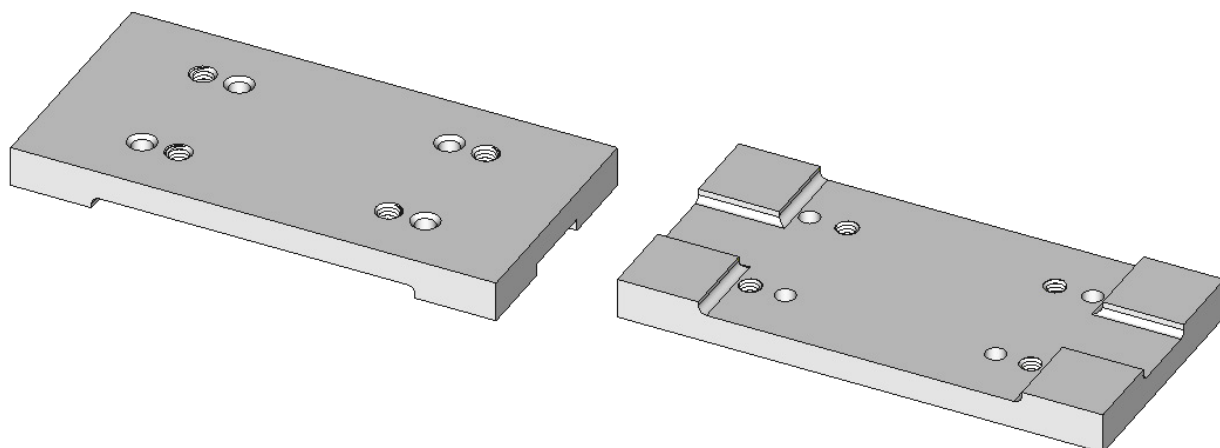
Основание с опорными выступами квадратного сечения
